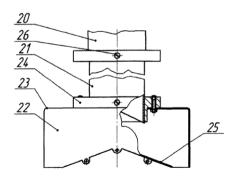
Стабилизатор уровня семян в высевающем устройстве вибрационного высевающего аппарата: 20 - патрубок цилиндрический; 21 - трубка цилиндрическая; 22 - стабилизатор; 23 - корпус стабилизатора; 24 - кольцо; 25 - двухскатный лоток; 26 - кольцо патрубка
